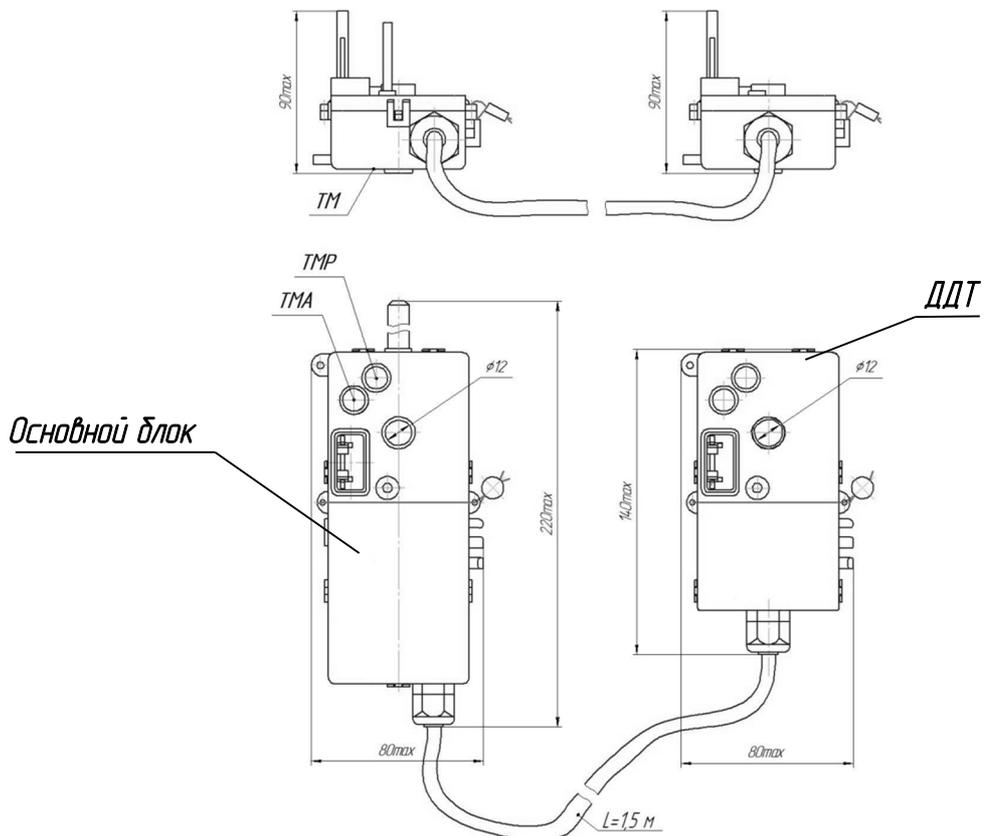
Габаритные и установочные размеры счетчиков, оснащенных ДДТ в корпусе тип «II»
